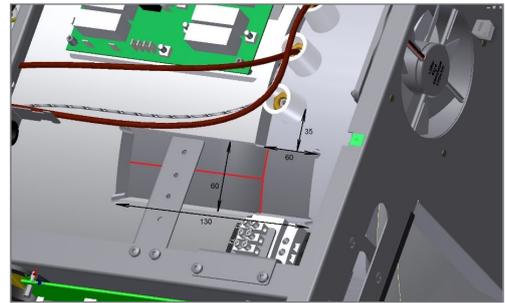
Draufsicht, Skizze für das Freilegen der Mantelnahte (Cliniclave 45)
